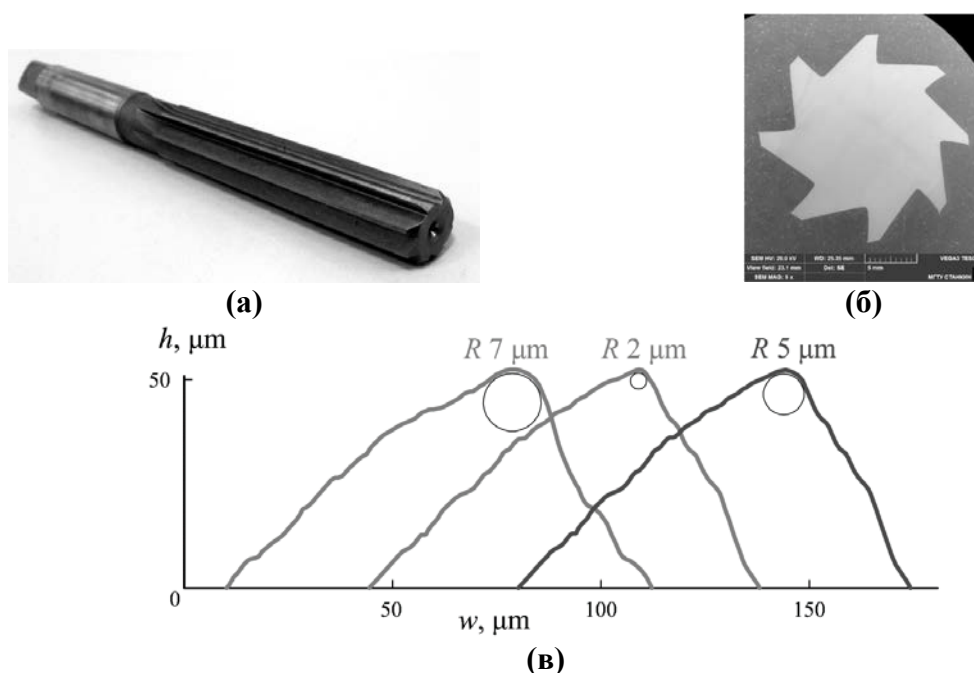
Развертка диаметром 16 мм из быстрорежущей стали Р6М5: (а) фотография развертки; (б) изображение сканирующего электронного микроскопа (SEM) поперечного сечения развертки; (в) профили режущих кромок развертки перед обработкой (слева) после заточки и азотирования (посередине) и после синтеза на азотированной поверхности 3-мкм толстого покрытия TiN (справа)
